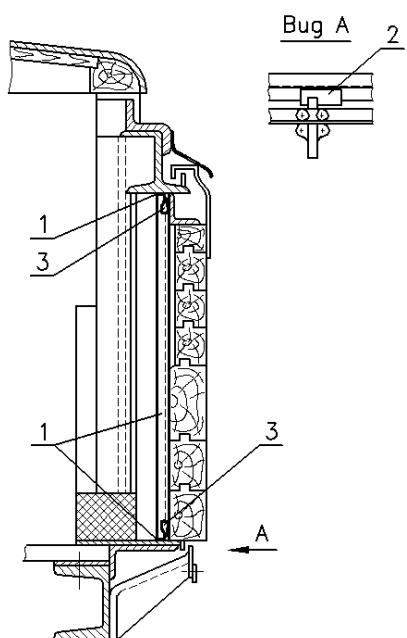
Заделка зазоров двери вагона, используемой для погрузки, бумагой
